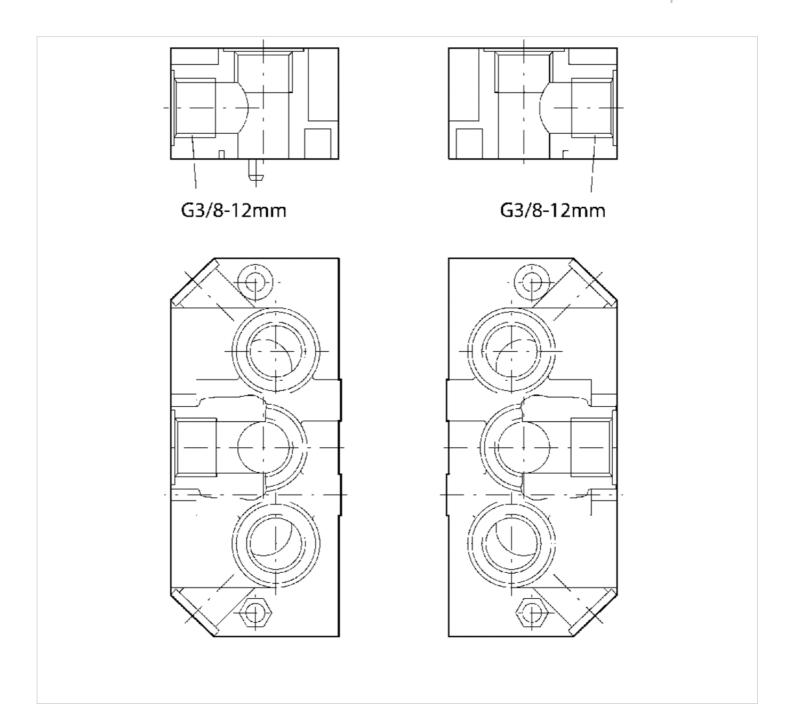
, Gewindeanschlüsse 1, 3 und 5 axial
